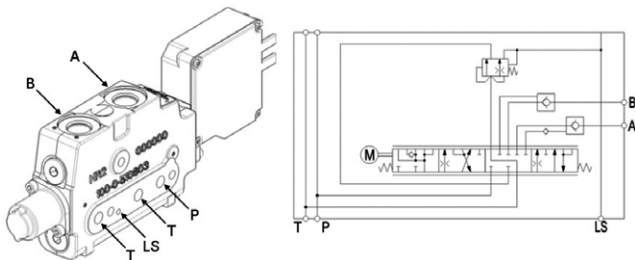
Wegeventil des Geräteträgers mit nachgeschalteter Druckwaage
